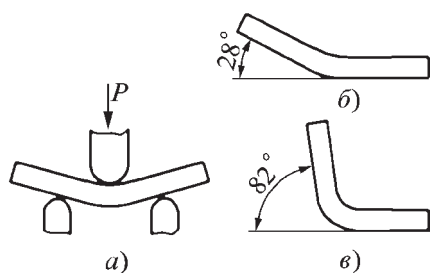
Схема испытаний для определения угла загиба образцов из быстрорежущей стали P9K5 (а) и примеры результатов испытаний (б, в)
